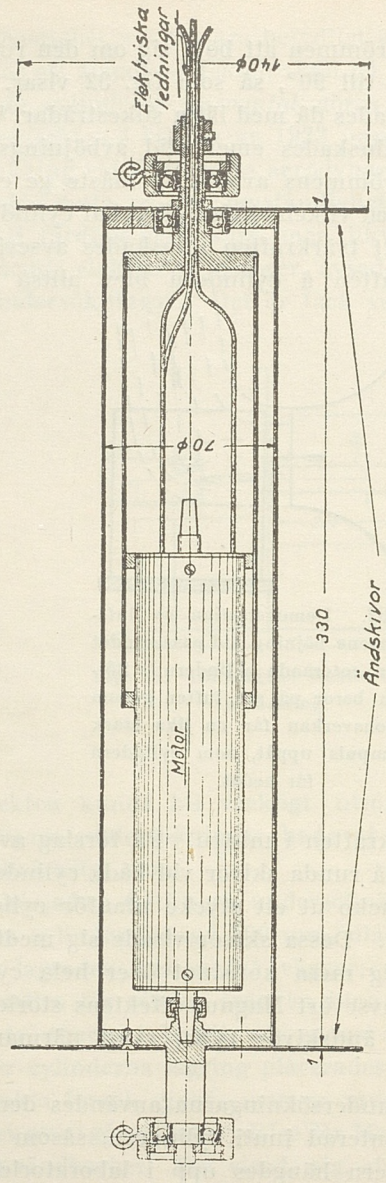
I Göttingen undersökt cylindrar med inbyggd motor.
